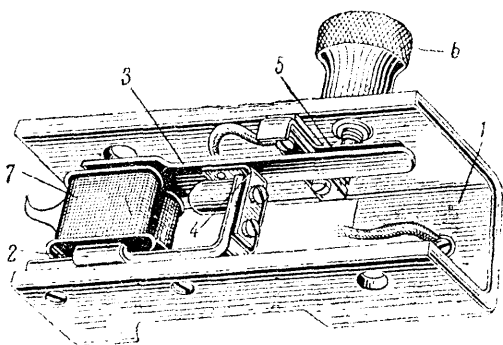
Общий вид зуммера аппарата УНА-Ф-28:
